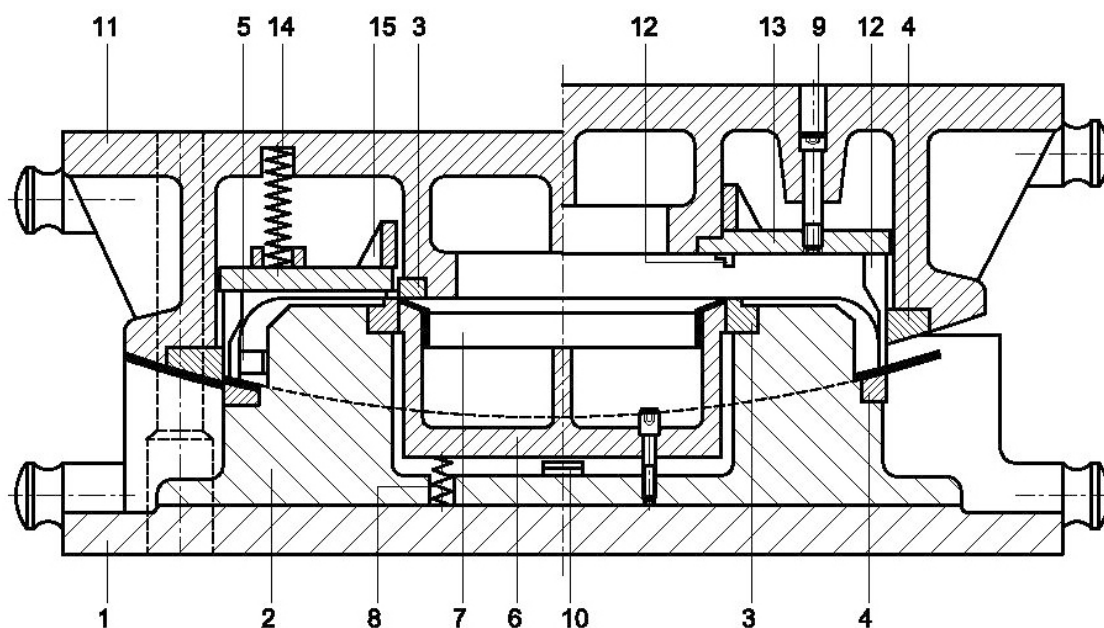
Beschneidwerkzeug – Großwerkzeug
